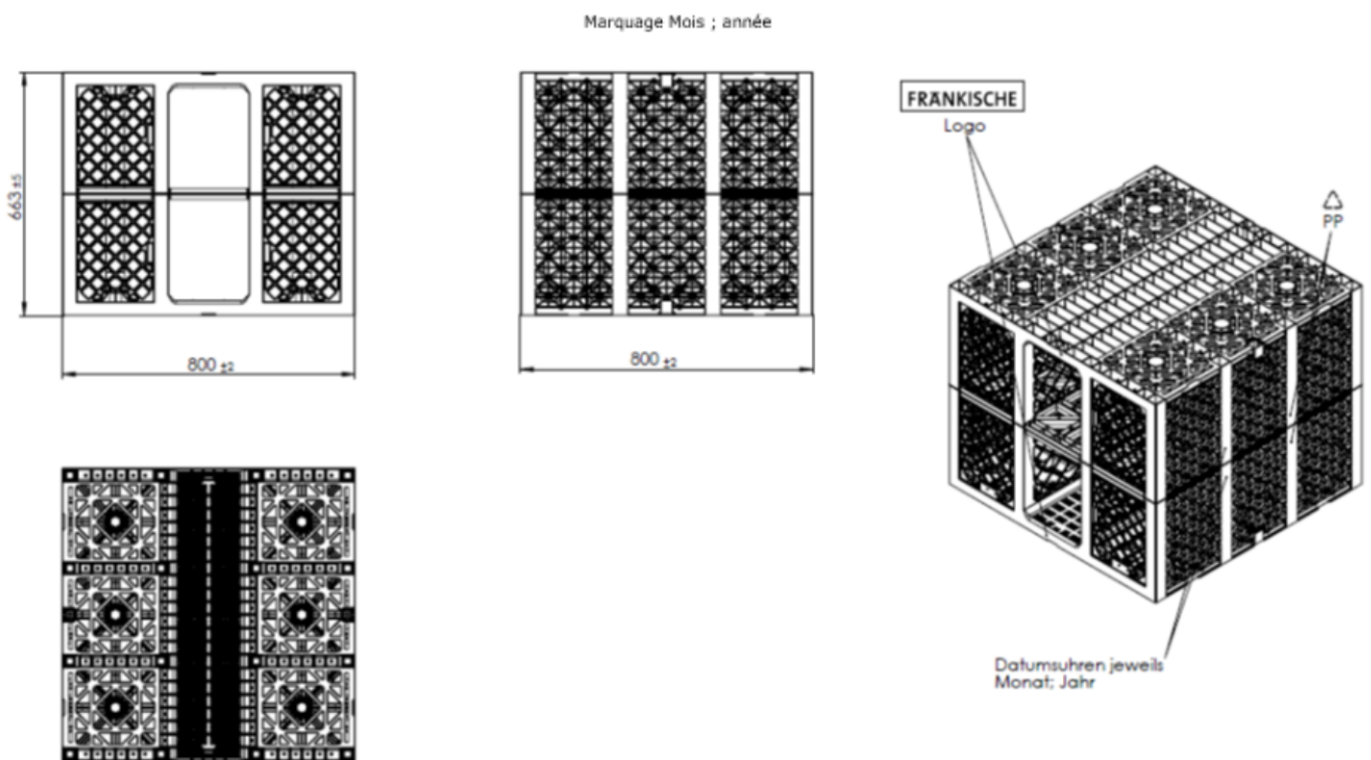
Caractéristiques dimensionnelles du demi-module Rigofill inspect
